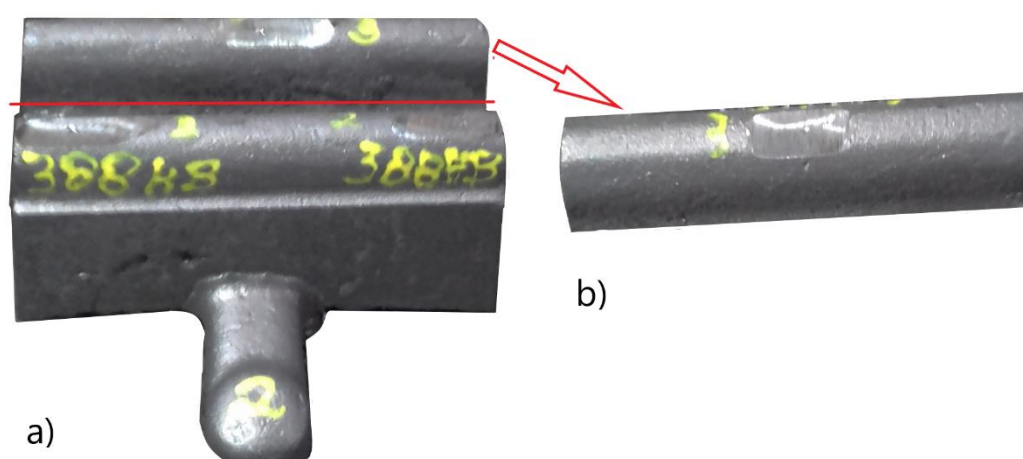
Esquema das regiões de corte dos corpos de provas no bloco fundido, sendo a) inteiro e B) serrados antes da usinagem final. Fonte: próprio autor.
